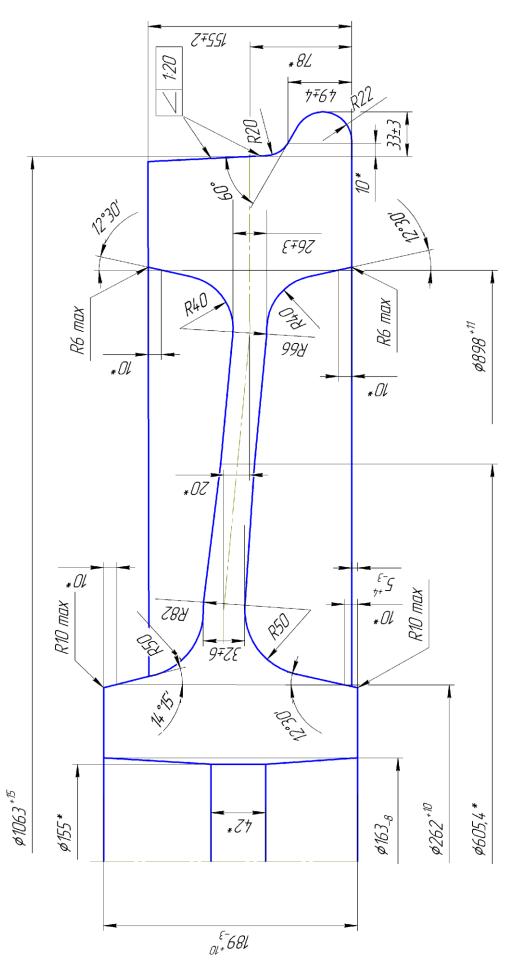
Колесо Ø 1070 мм без механической обработки, для Ø 1050 мм по чертежу № КР-0032-16. Масса колеса 573 кг
